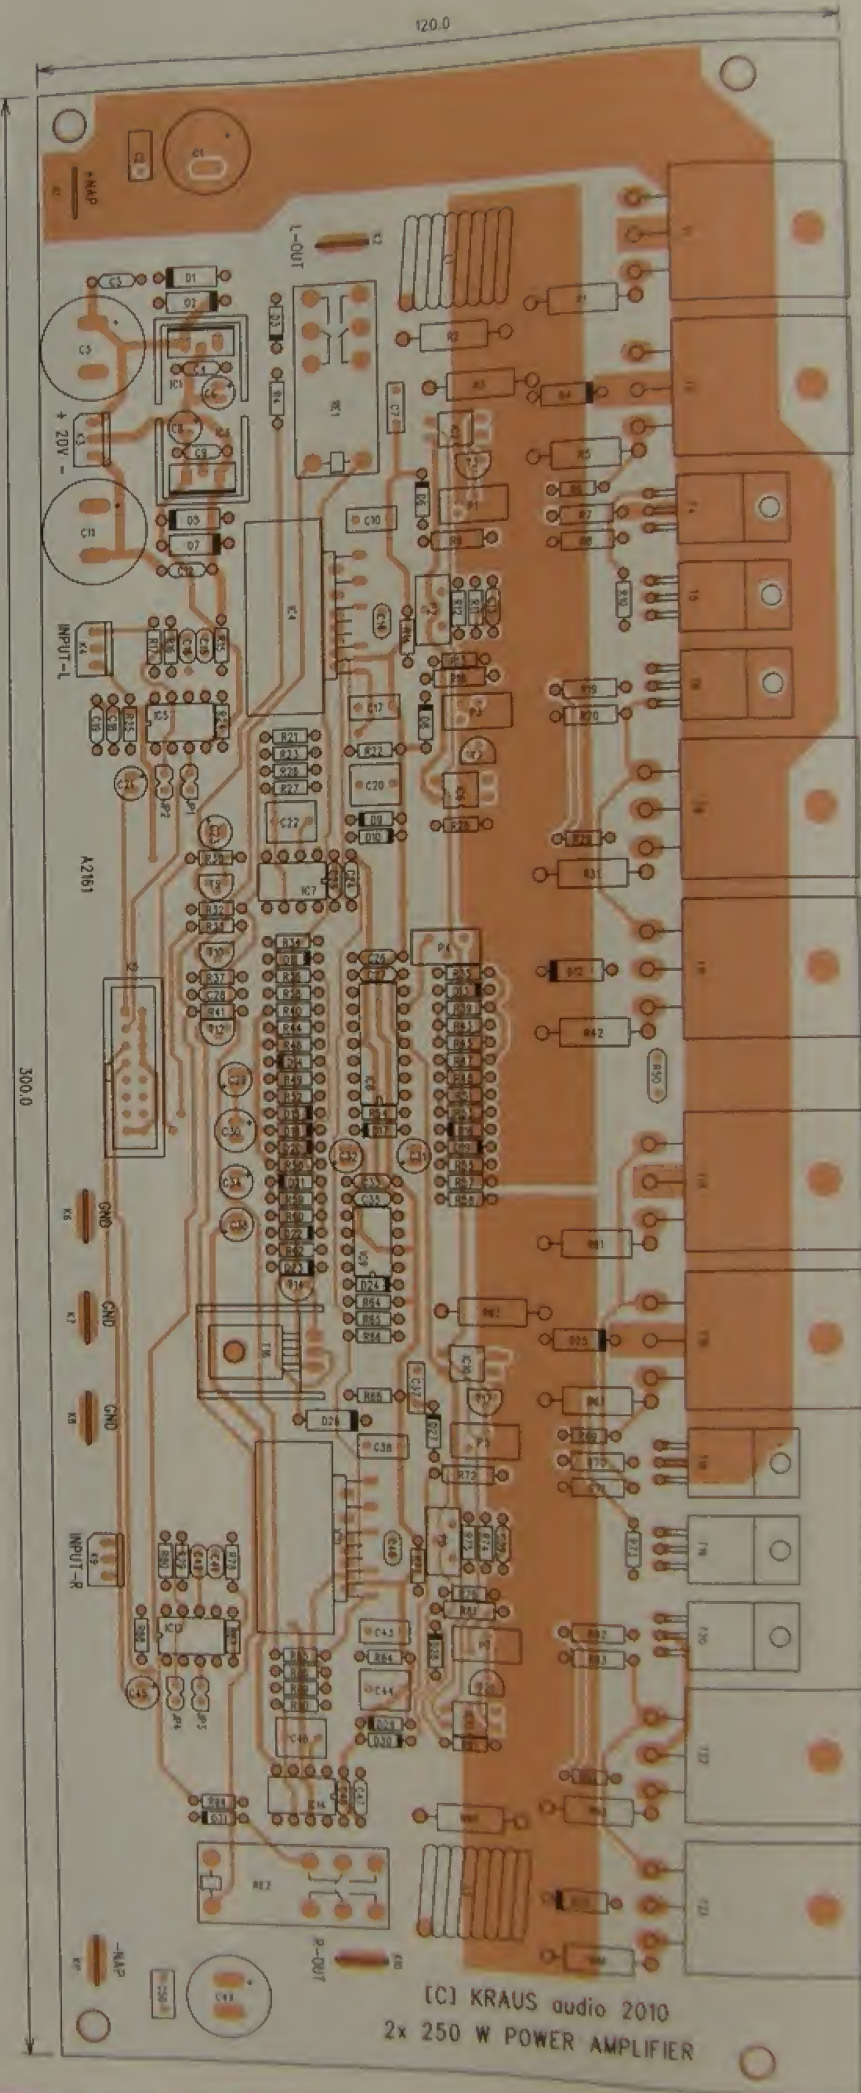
Obrazec desky spojů ze strany spojů (BOTTOM)
